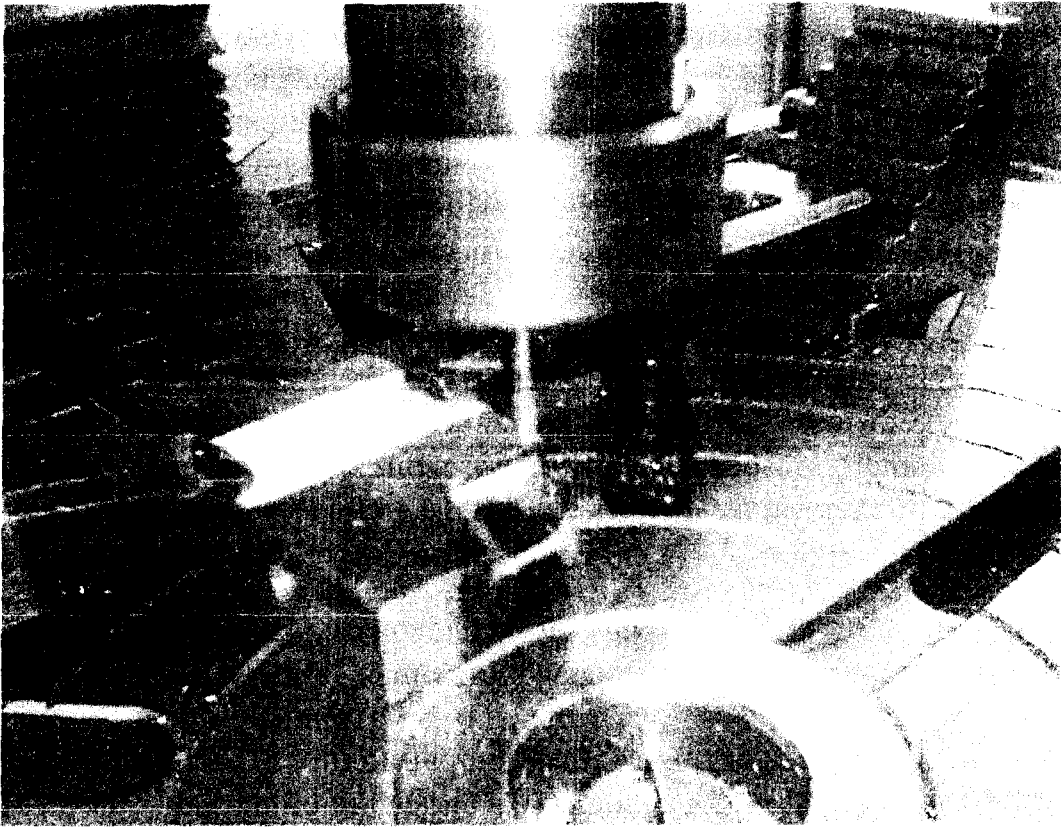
Изготовление черного электрода для электроискровой обработки заготовки
